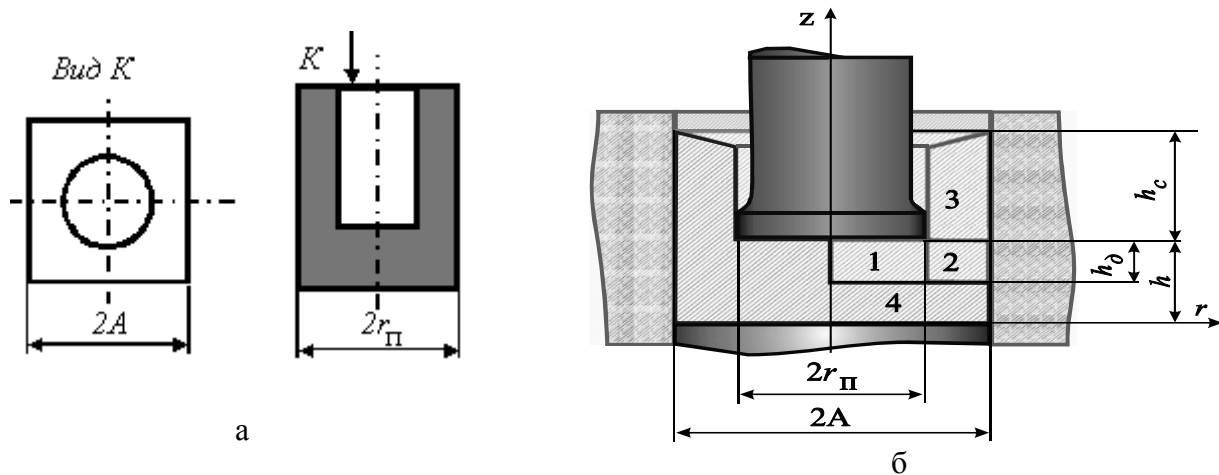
Схема выдавливания детали (а) и разбивка заготовки на зоны (б)
